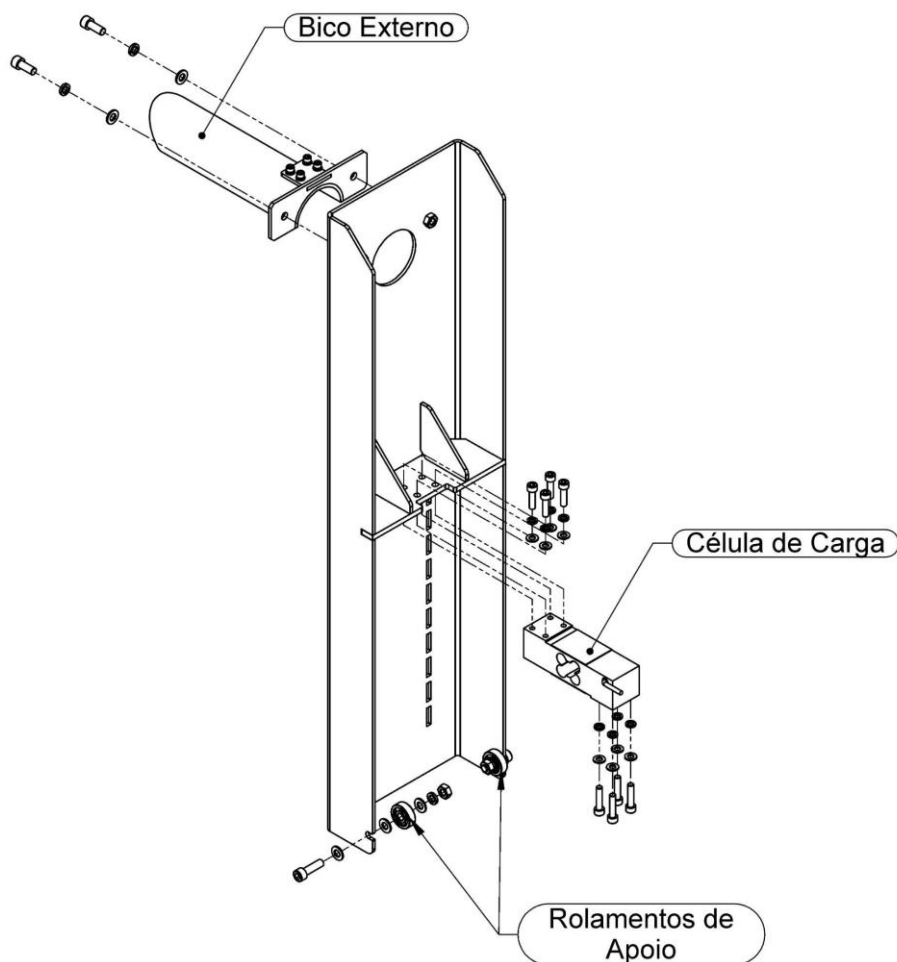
Vista explodida em corte do subconjunto dosagem.
